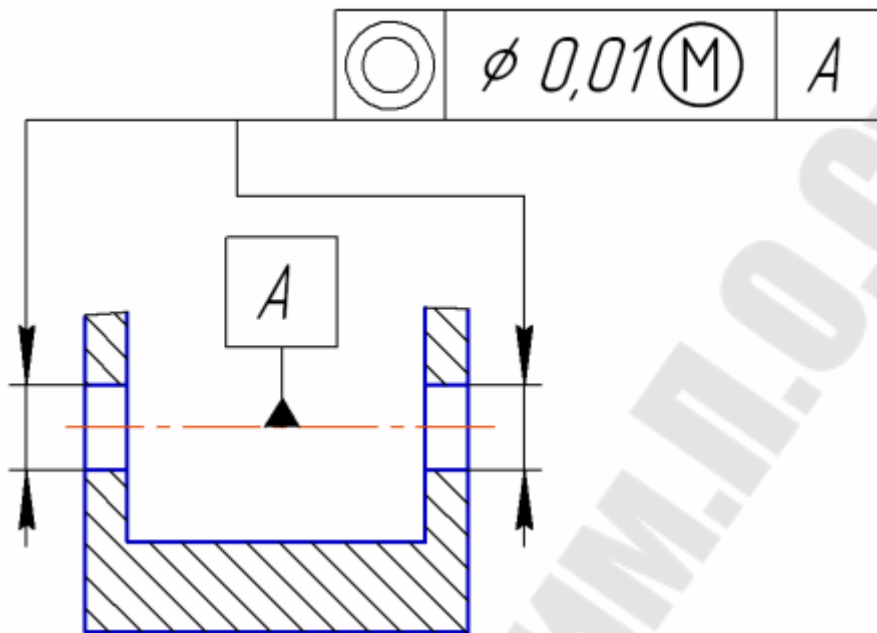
Простановка допуска расположения поверхностей
